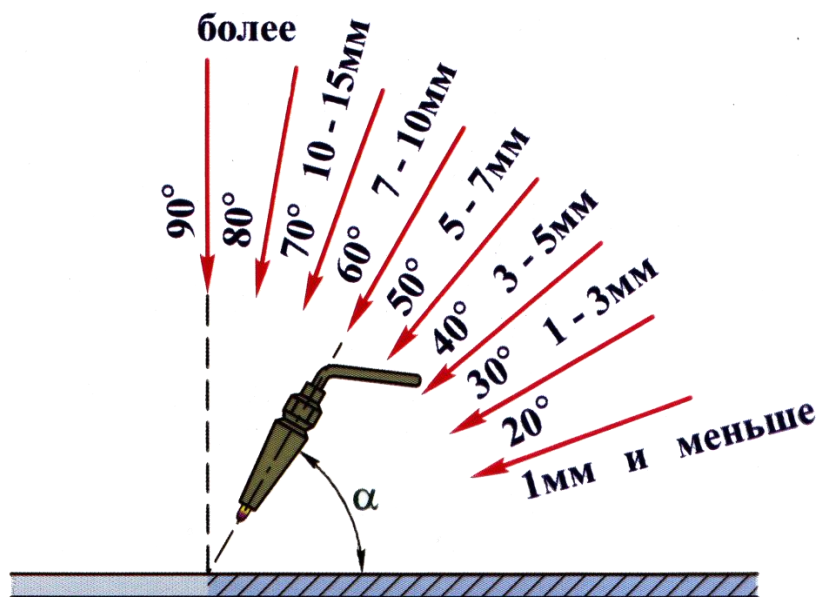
Выбор угла наклона сварочной горелки для левого способа
